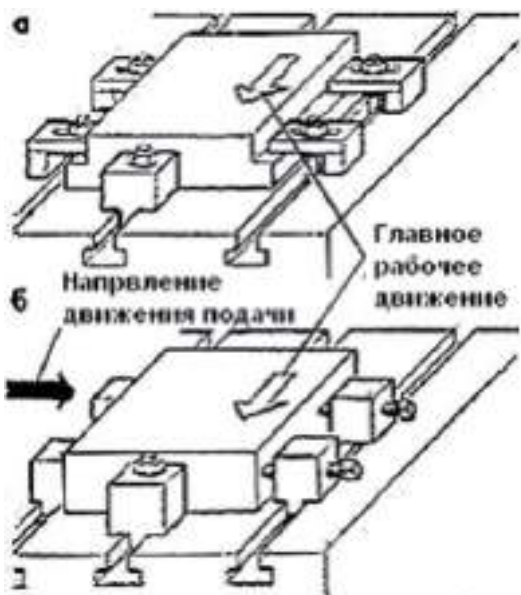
Примеры закрепления заготовок прихватами, прижимами и упорами
